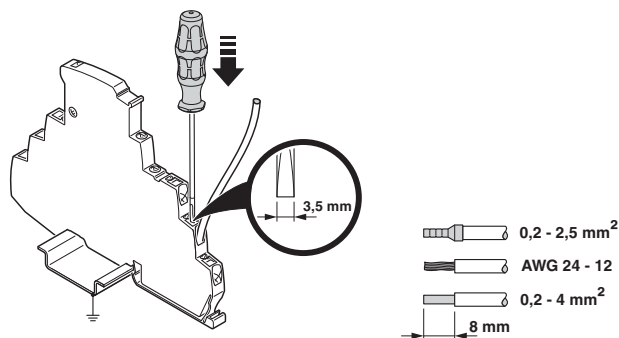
Variante di collegamento connessione Push-in (larghezza costruttiva 6 mm)
